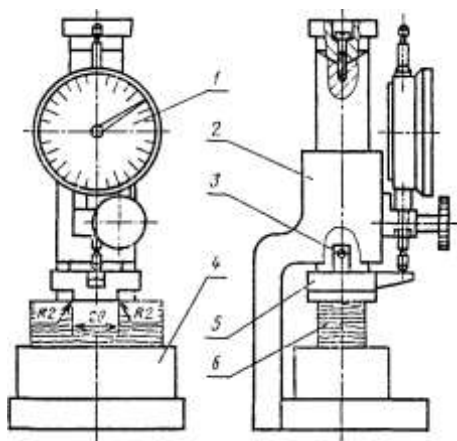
9. Приспособление к испытательной машине. 1 – индикатор; 2 – корпус; 3 – шток; 4 – подставка; 5 – съемный пуансон; 6 – образец
